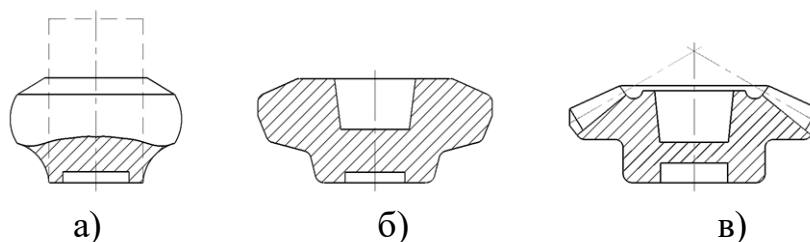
Схема переходов горячей объемной штамповки зубчатого конического колеса:
